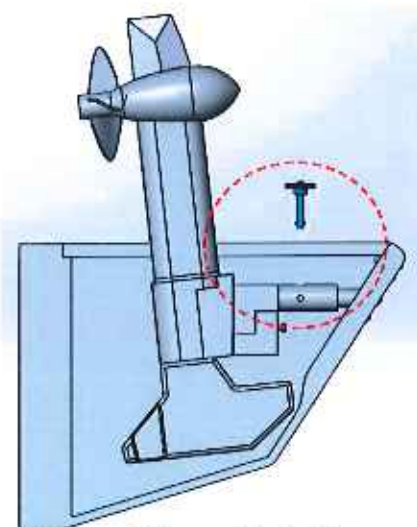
Seitenansicht des Motors mit Kugelsperbolzen
